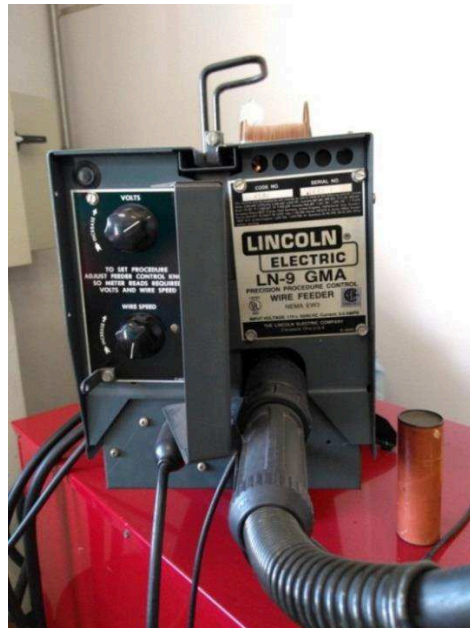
TRANSFORMADOR DE SOLDA
